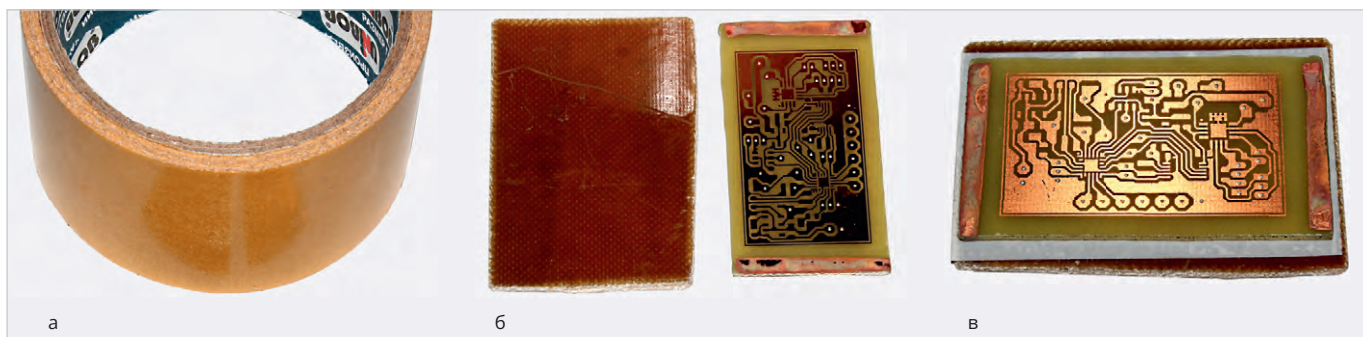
Приклеивание заготовки к стеклотекстолитовой пластине: а – двусторонний тонкий скотч, б – пластина и заготовка, в – склейка
